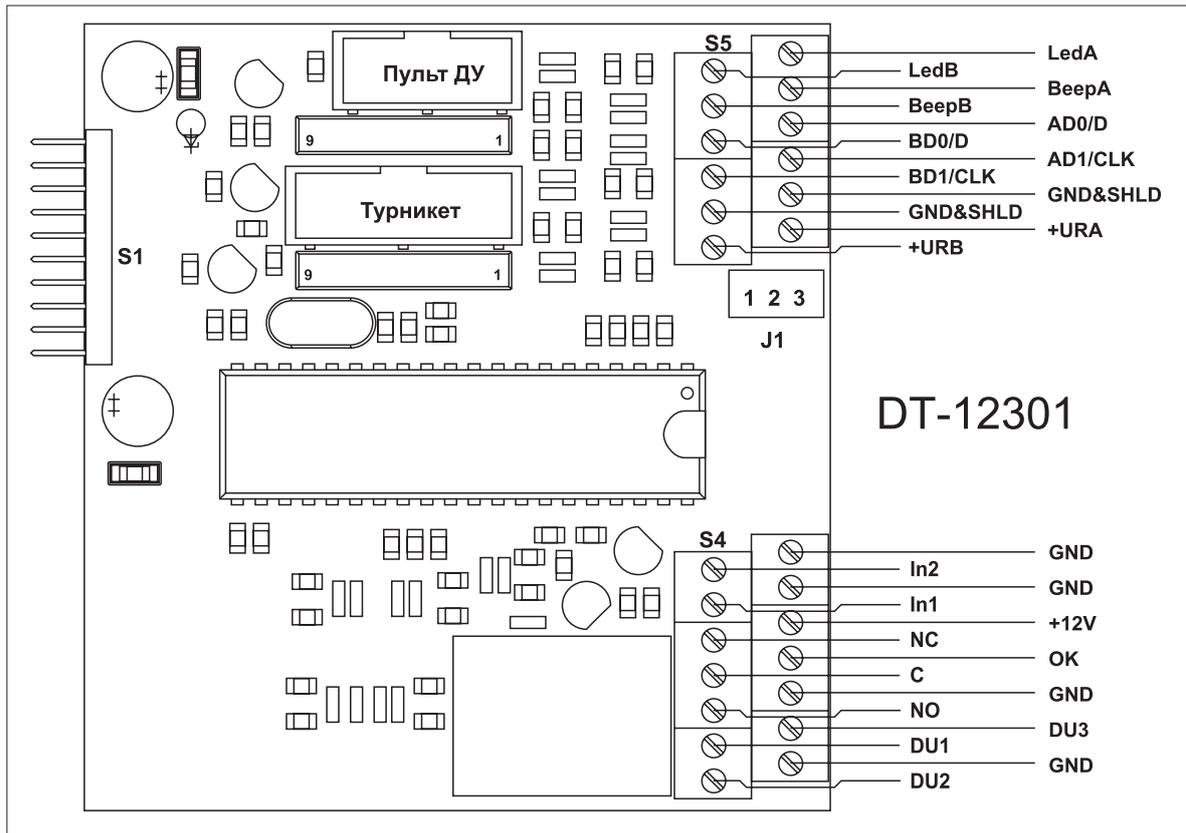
Внешний вид печатной платы DT-12301 в сборе
